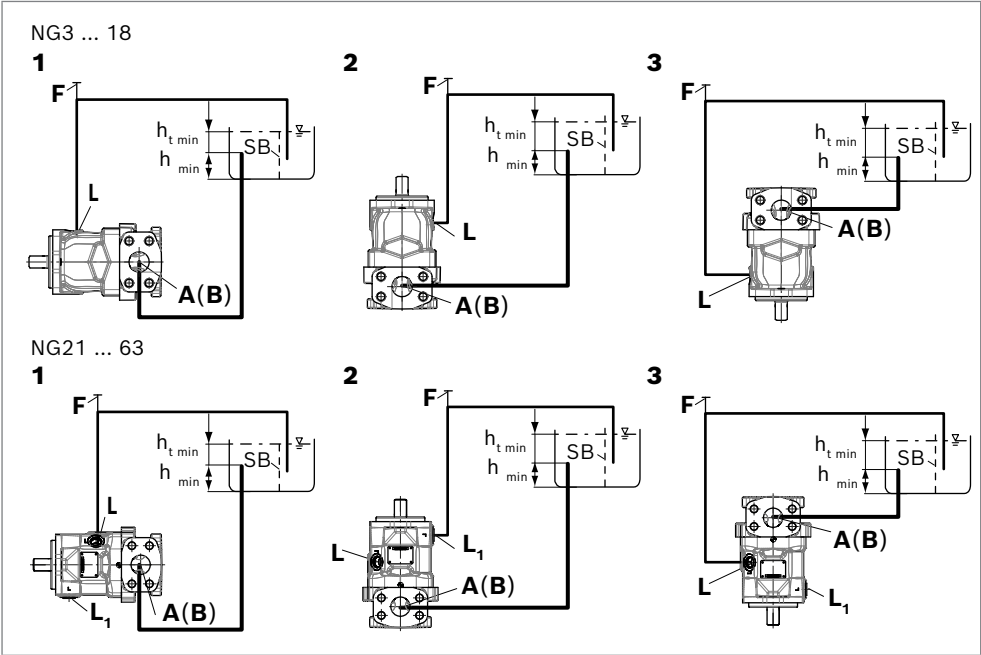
Untertankeinbau A10FZG mit Einbaulage 1–3
